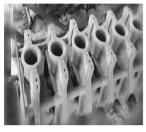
长江铸钢砂壳型裸浇 Fig.1 Pouring shell mold assemblies made by Changjiang cast steel sand
